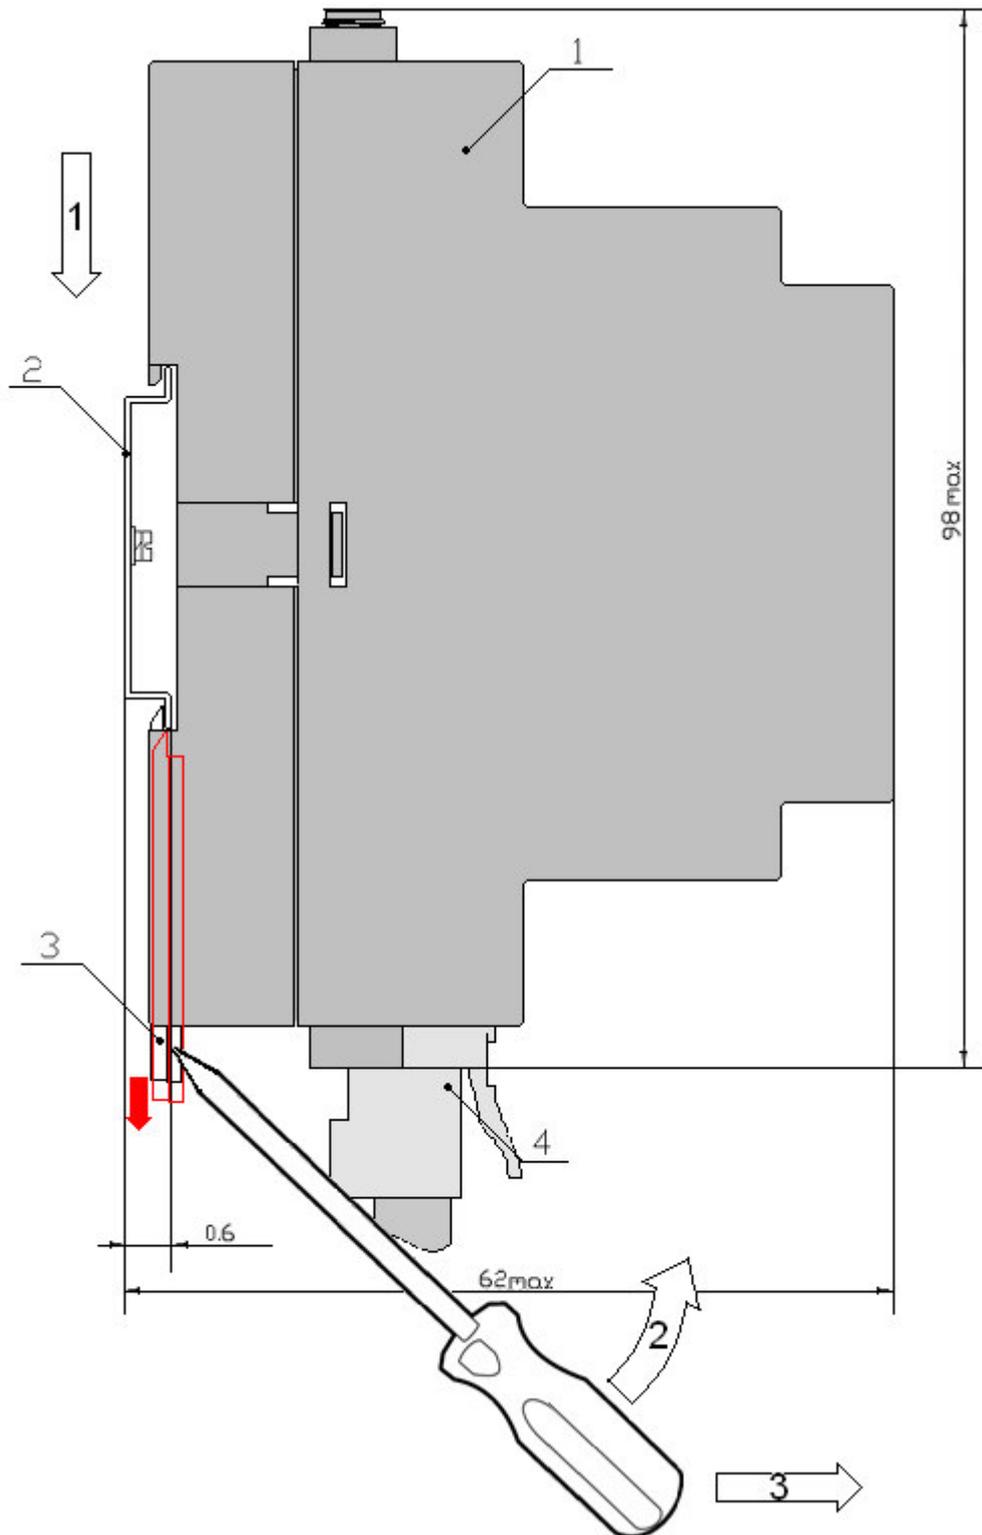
Контроллер. Габаритно-установочный чертеж. Вид спереди
